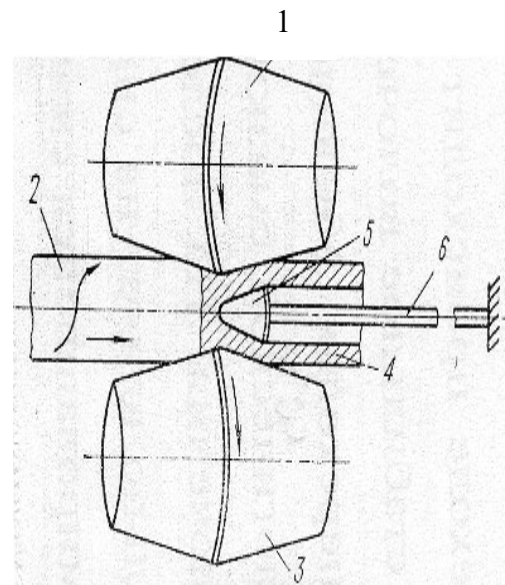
Схема поперечно-гвинтової прокатки (вид сверху): 1 – лівий валок; 2 – заготовка; 3 – правий валок; 4 – гільза; 5 – оправка; 6 – штанга.
